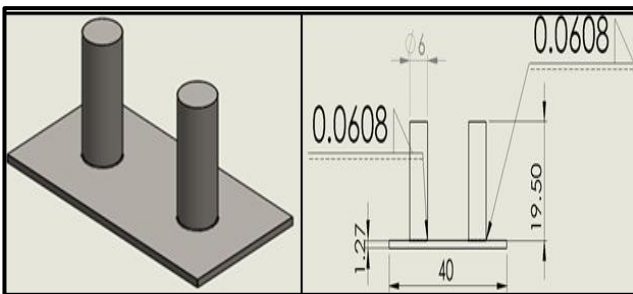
Indicación de soldadura de la pieza MBC-C-24-3.
